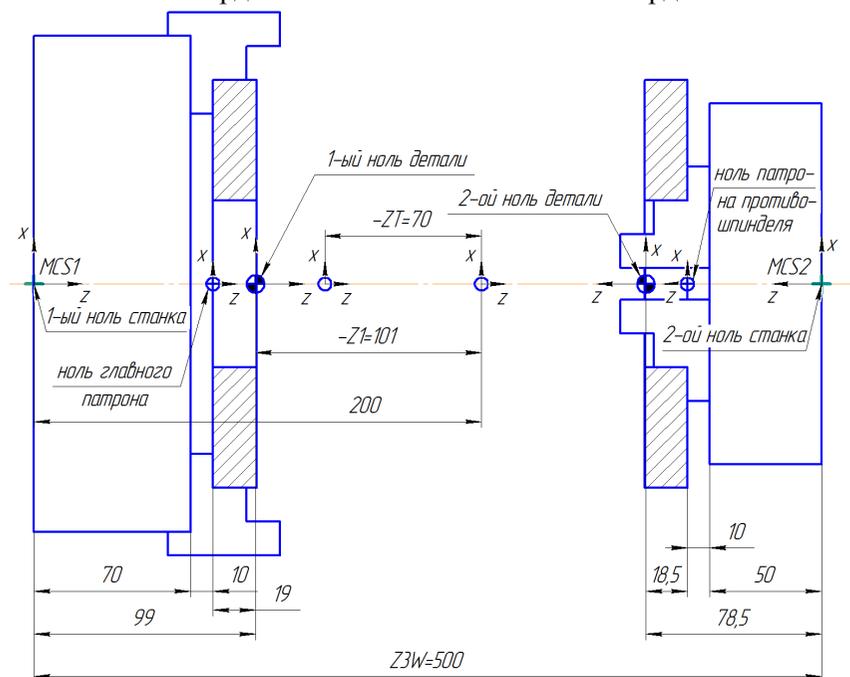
Схема расположения нулевых точек: станка, патронов и детали
